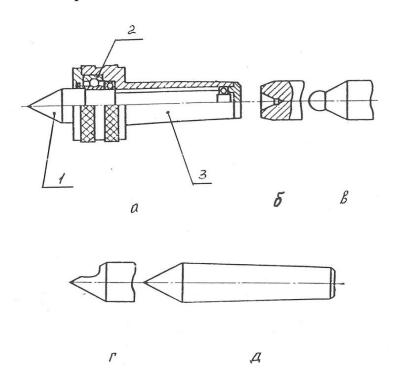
Центра: а – вращающийся; б – обратный; в – со сферической рабочей частью; г – срезанный; д – упорный
